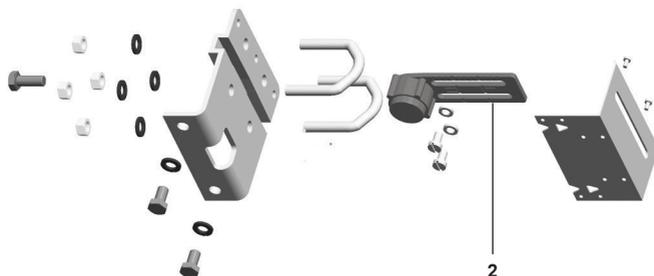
Kit di montaggio a colonna per un attuatore lineare
